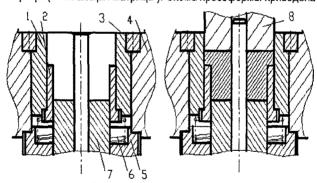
Схема прессования. 1 - матрица; 2,7 - составные элементы нижнего пуансона; 3 - кольцо; 4 - обойма; 5 - упор; 6 - пружина; 8 - верхний пуансон.
